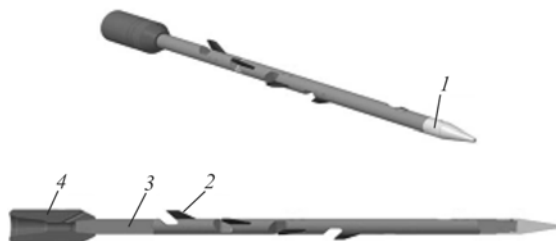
Общий вид удочки ловильной для кабеля внутренней:
